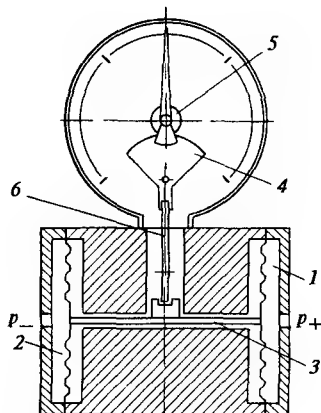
Мембранный двухкамерный показывающий дифманометр:
